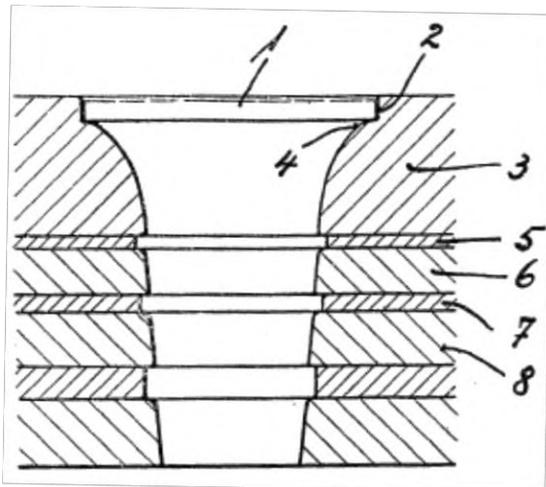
Patent: „Ziehwerkzeug mit traktrixförmigem Einlauf zum Ziehen dicker Bleche“ 1930 [DPMA]
